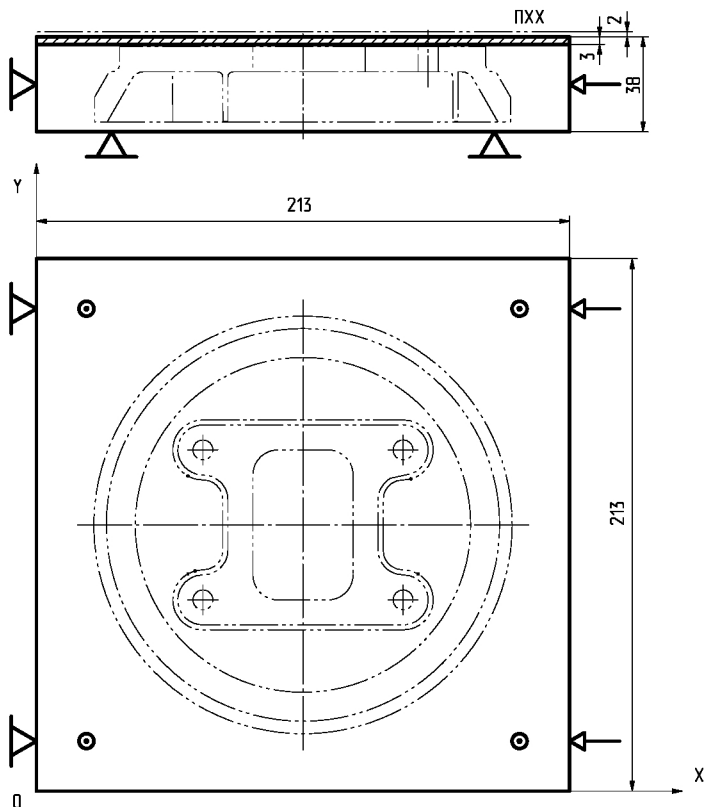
Эскиз фрезерной операции обработки чистовой базы
